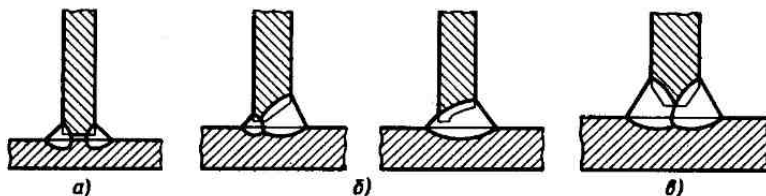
Подготовка кромок угловых швов тавровых соединений:
